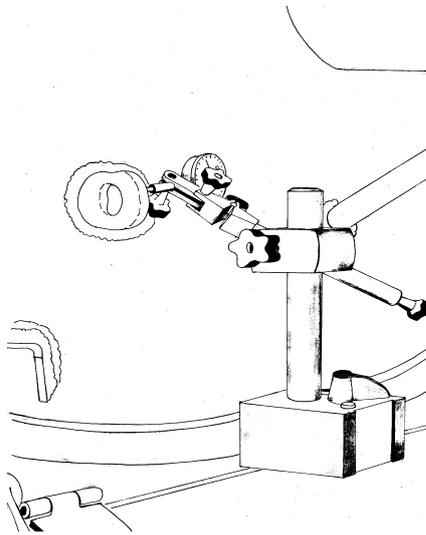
Установка штатива с индикатором ИЧ на БМД-2 для проверки жесткости привода ГН
